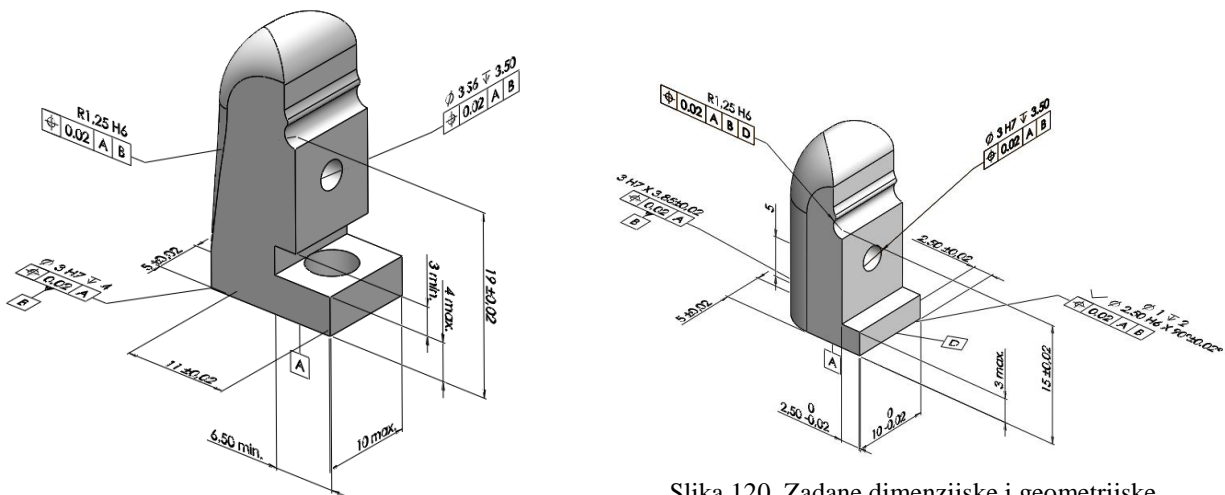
Zadane dimenzijske i geometrijske tolerancije Podnožja nosivog stola
